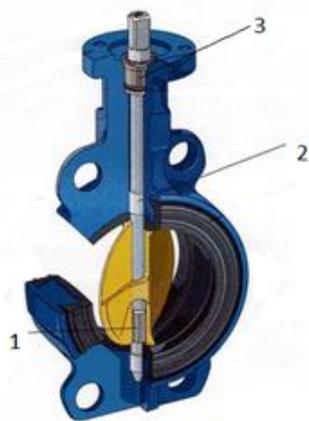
Поворотная заслонка: 1 – поворотный диск; 2 – подшипник; 3 – стопорное кольцо
